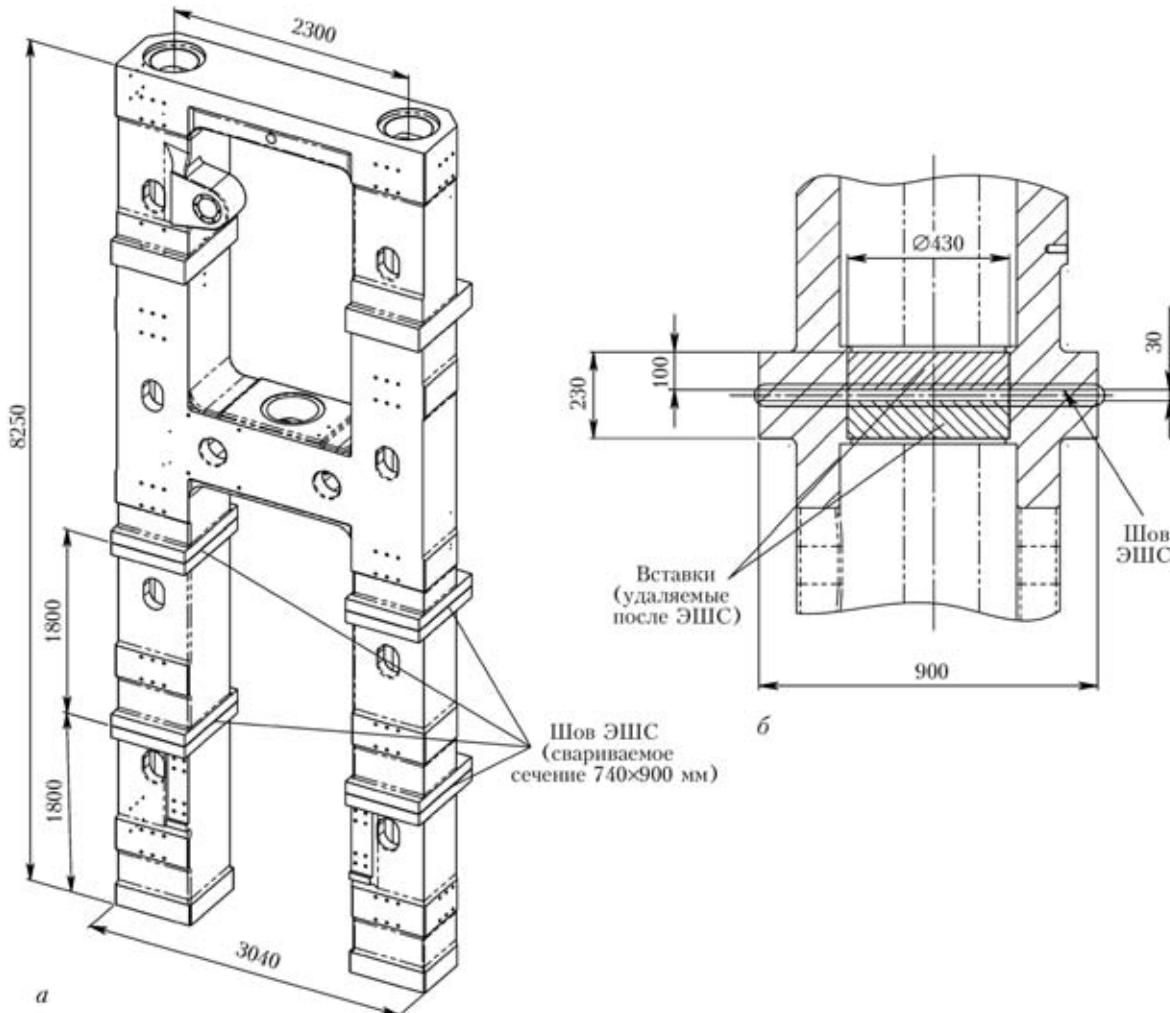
Эскиз сваренной ЭШС проставки (а) и поперечное сечение сварного соединения (б)
